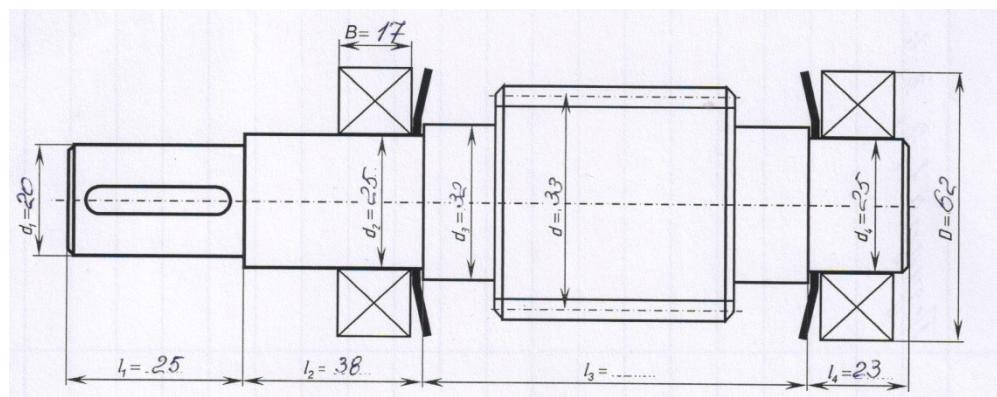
Конструкция быстроходного вала цилиндрического редуктора.
